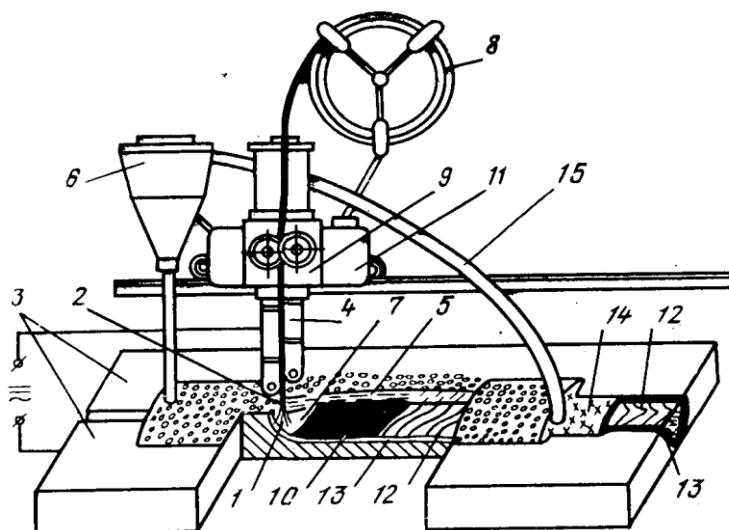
Схема автоматической сварки под слоем флюса:
